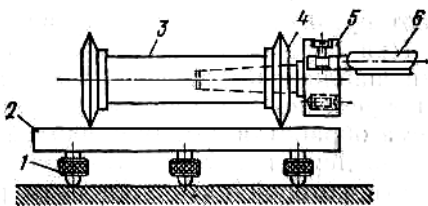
Приспособление для статической балансировки фрезы с патроном:
